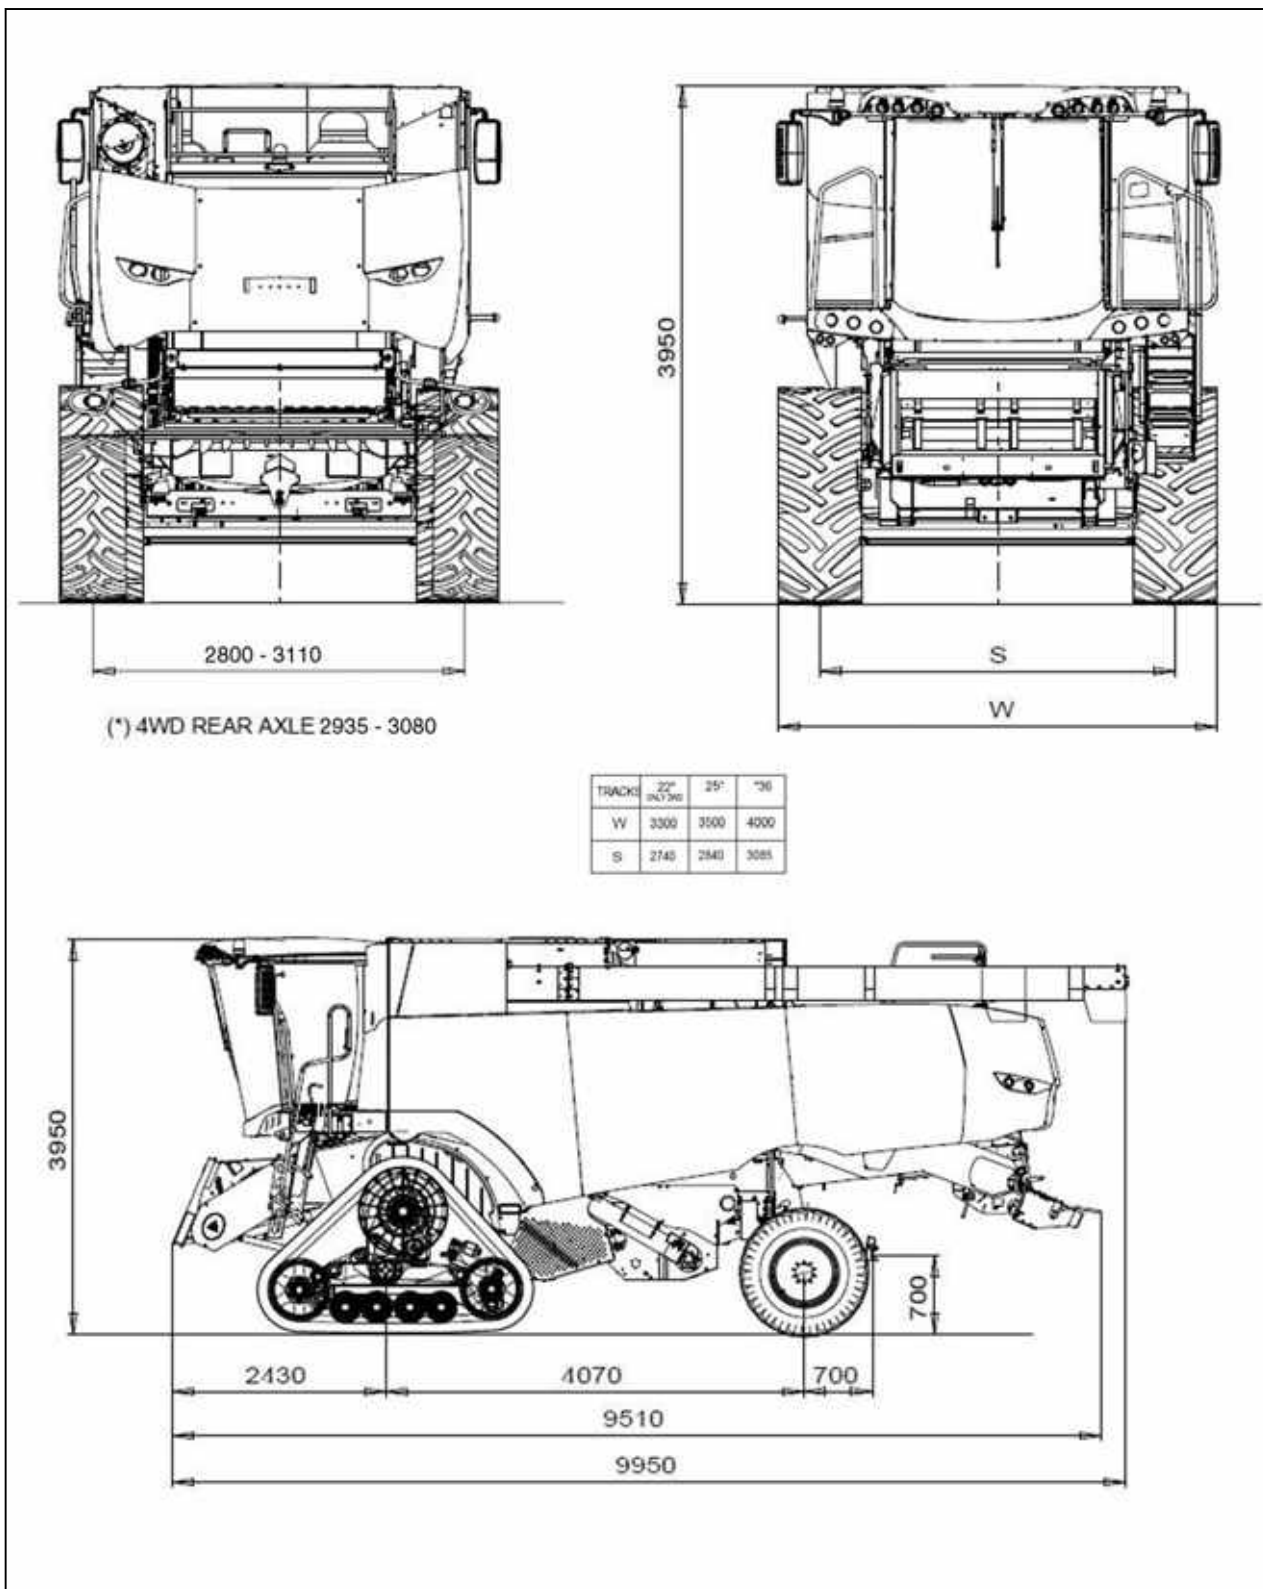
Dimensioner for maskine med bælter; front, bag, side
